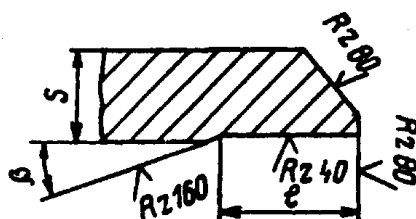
Конструктивные размеры кромки трубы, обработанной под подкладное кольцо
